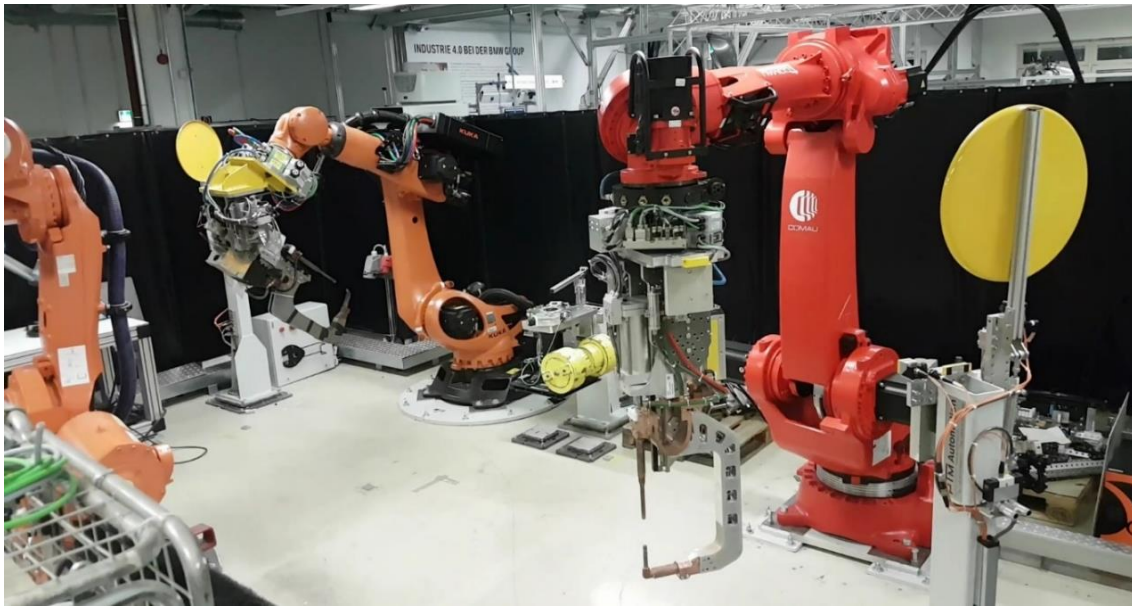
Roboter im Testbetrieb einer Punktschweißapplikation mit Werkzeugwechsler
